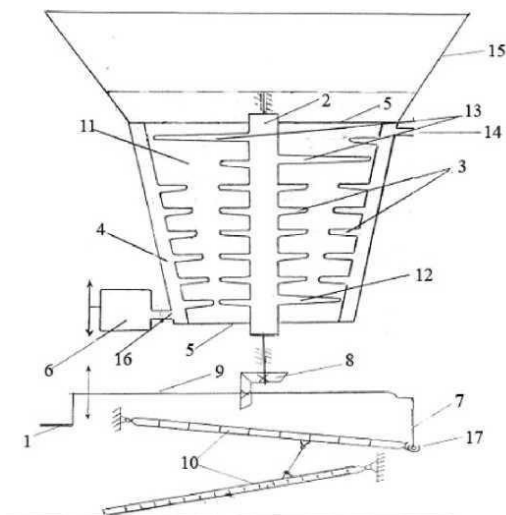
Принципова схема шишко-подрібнювача Попова А. Т.:
